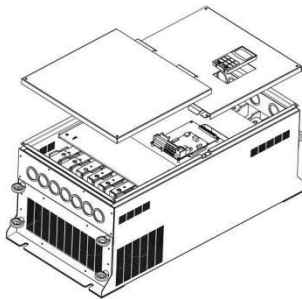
Dibujo de desmontaje de la placa de cubierta inferior de la carcasa de placa metálica
